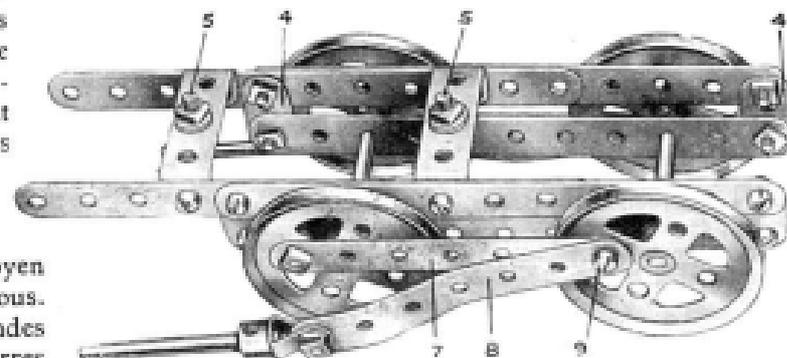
Châssis de la locomotive « haut-le-pied ».
